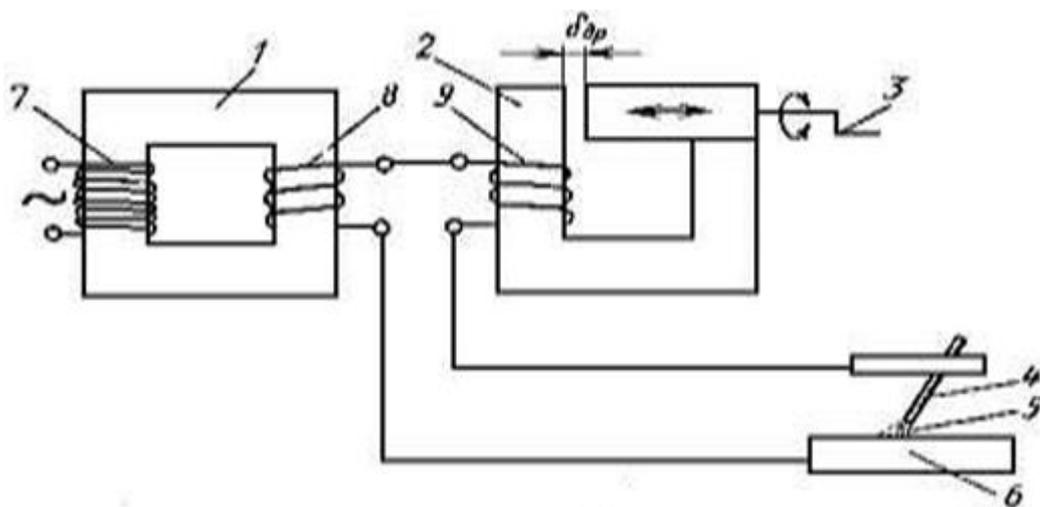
Схема сварочного поста трансформатора СТЭ
